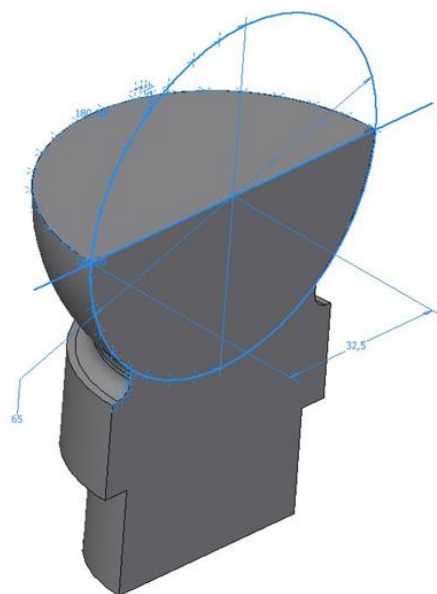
Двохопорний шворінь СЗП зі сферичною поверхнею контакту.
